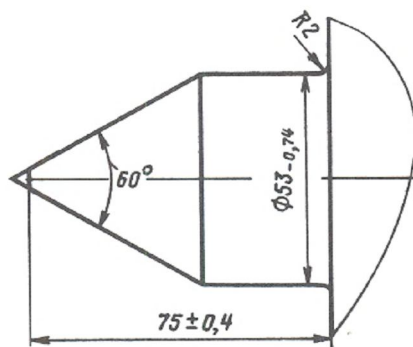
Конусная часть центра пиноли колесотокарного станка
